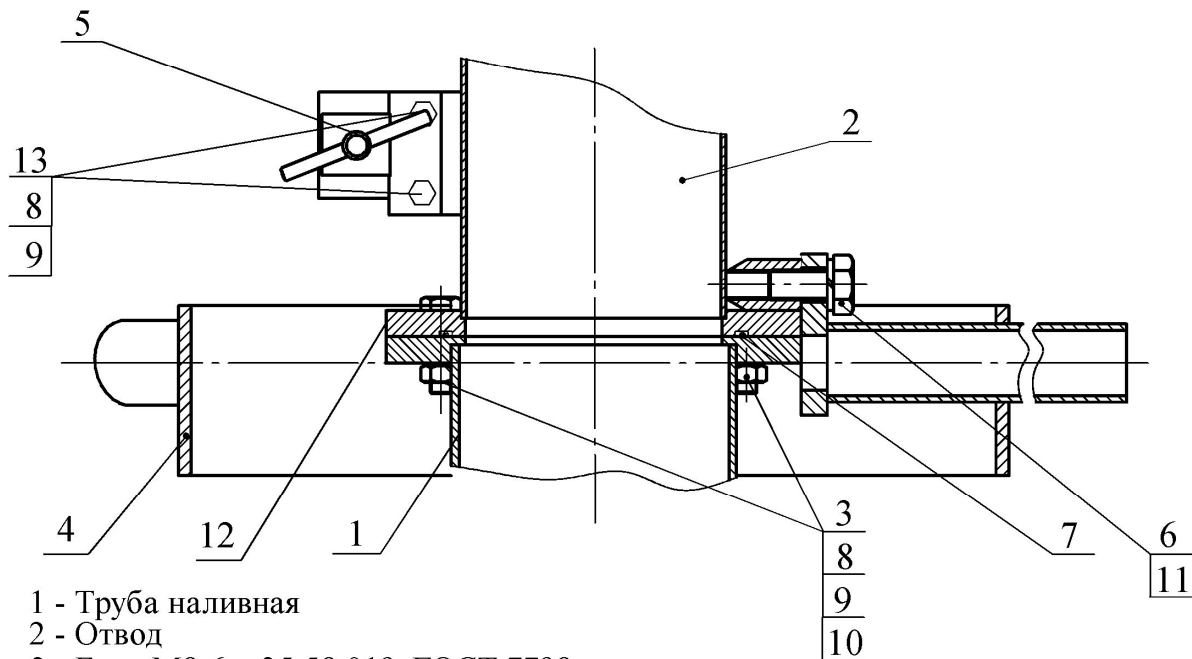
Шарнир соединительный фланцевый тип 2, 4
